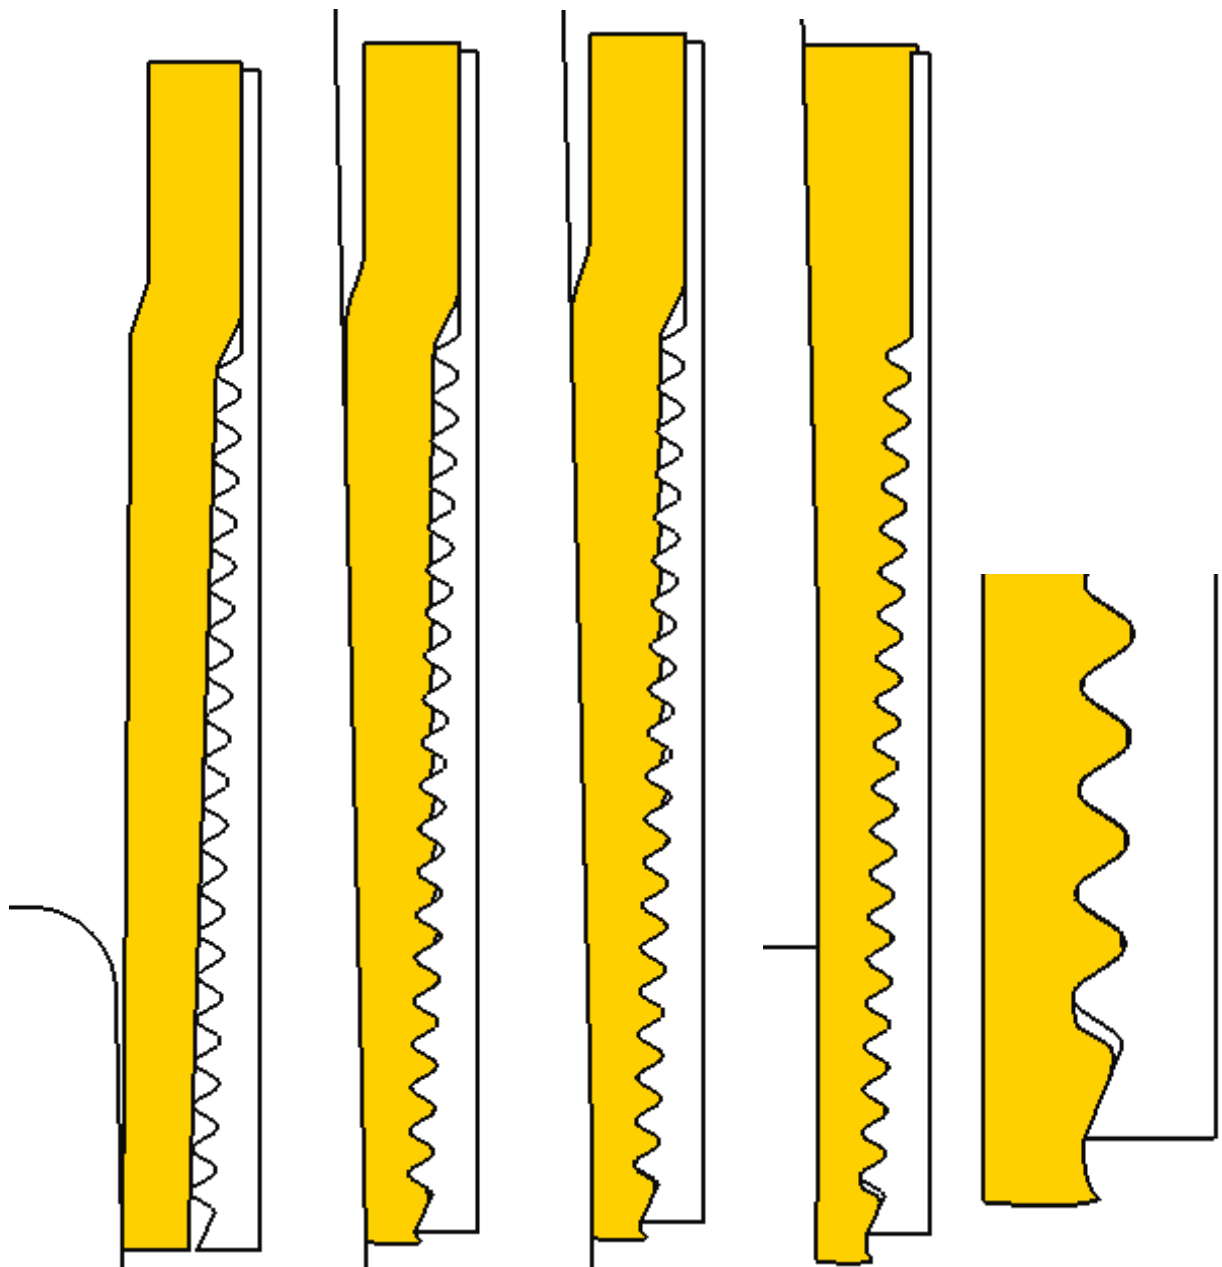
Последовательность оформления контура резьбы на предварительно профилированной заготовке. Конусность заготовки 1:100, наружный диаметр цилиндрической части 73 мм, толщина стенки 5,5 мм, длина конической части 55 мм (по внутренней поверхности)
